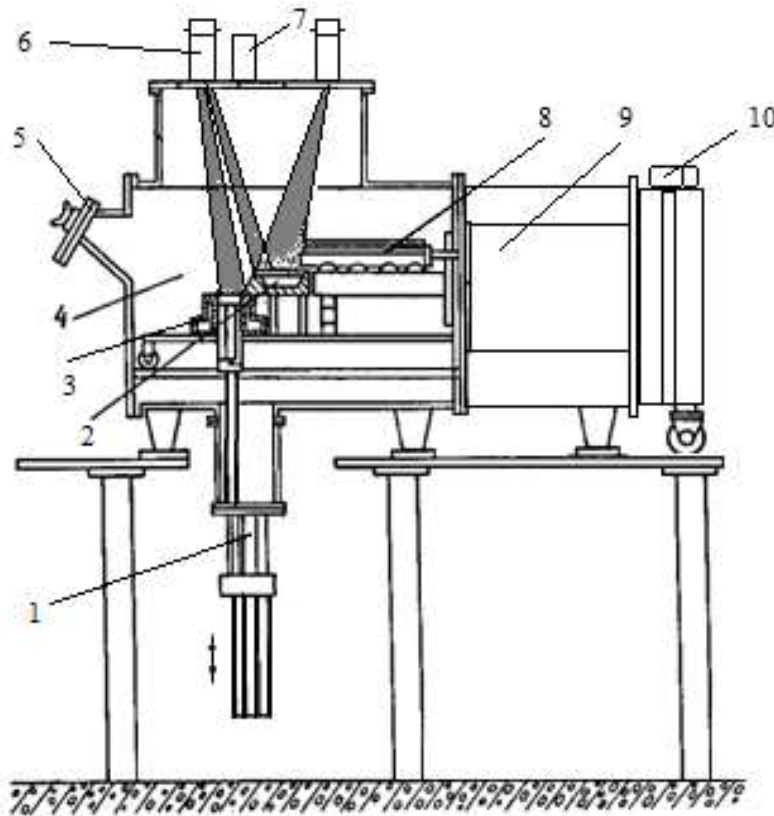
Схема електронно-променевої установки UE-208M. 1- механізм витягування зливка, 2 - проміжна ємність, 3 - кристалізатор, 4 - камера плавки, 5 – оглядова система, 6 - електронно-променеві гармати, 7 – водяний реостат, 8 - витратна заготовка, 9 – камера заготовки, 10 - механізм подачі заготовки
